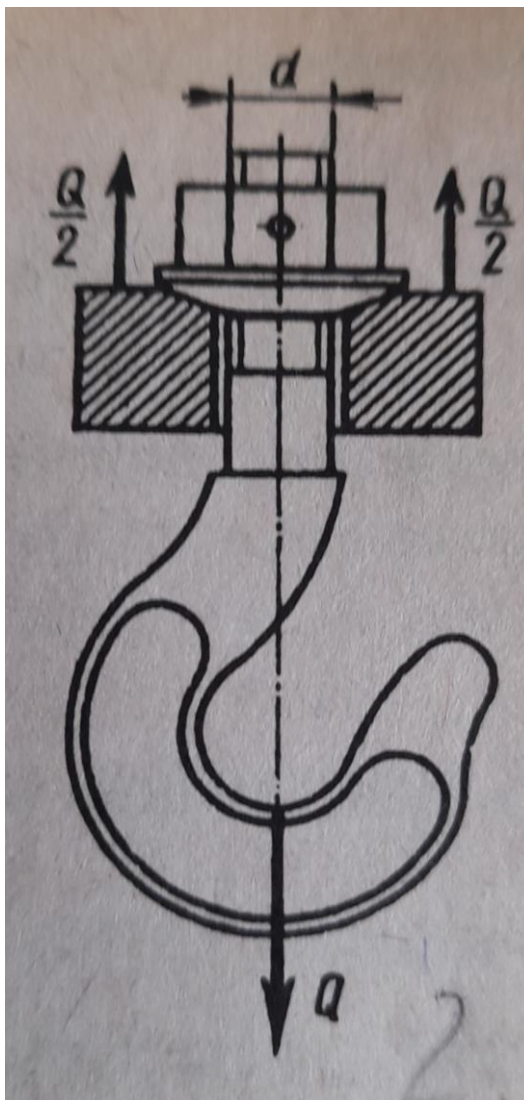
Расчетная схема незатянутого болтового соединения
